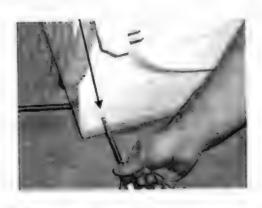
Удаление винтов, крепящих корпус к основанию машины
